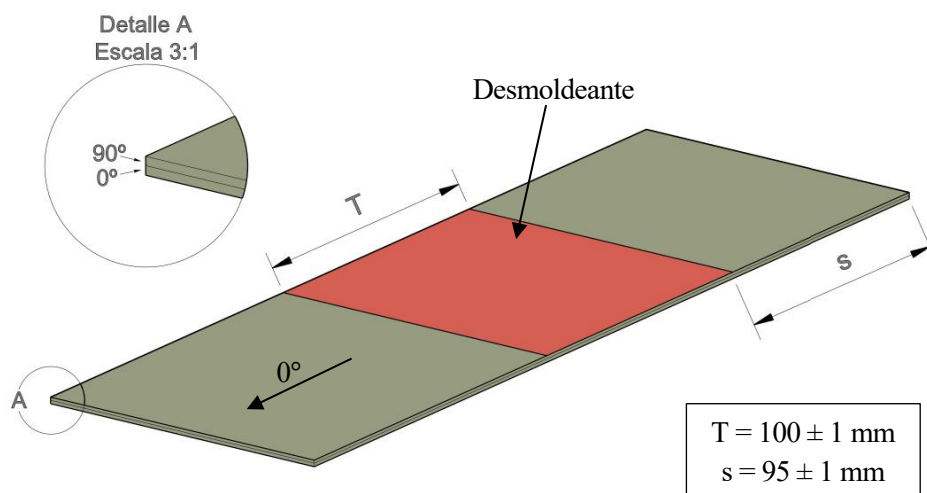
Apilado de la lámina desmoldeante central del panel 1
